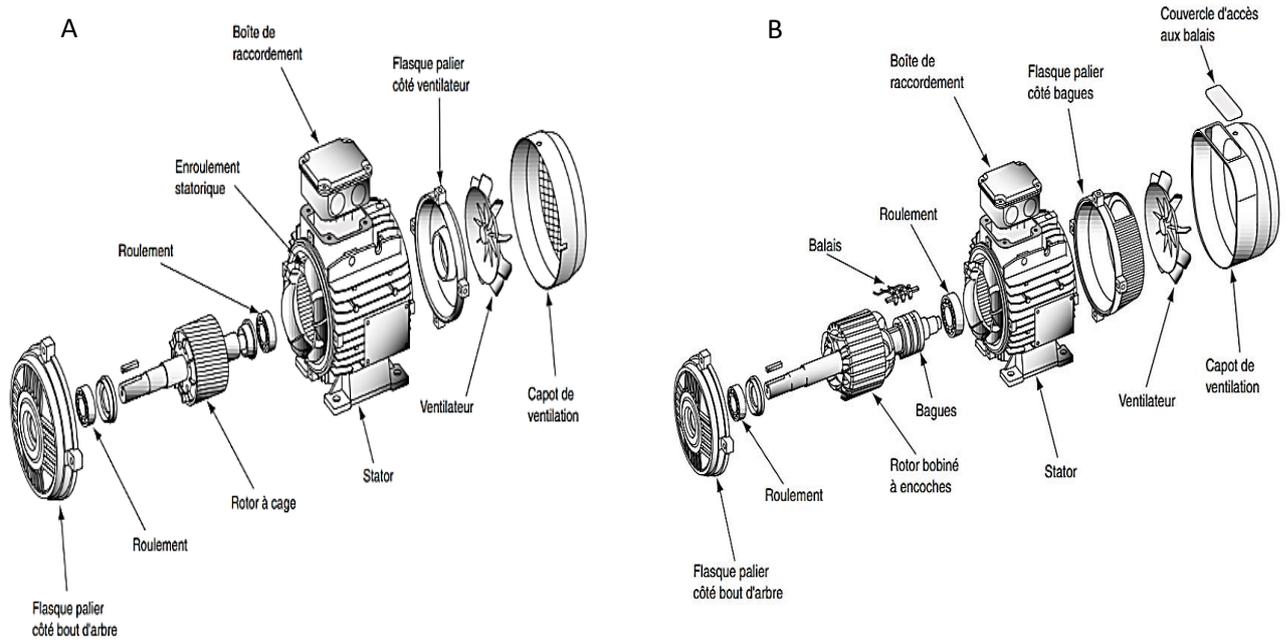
Machine asynchrone à rotor à cage d'écureuil (A) et à rotor à bagues (B)
